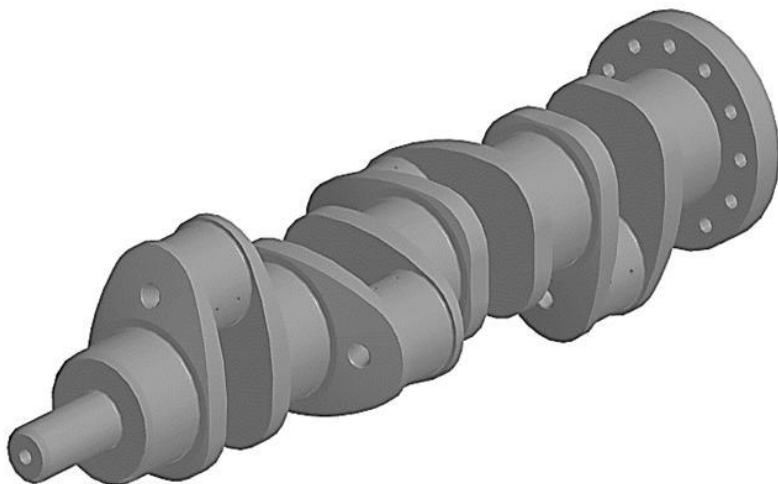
Изометрия коленчатого вала двигателя 8ЧН14/15
